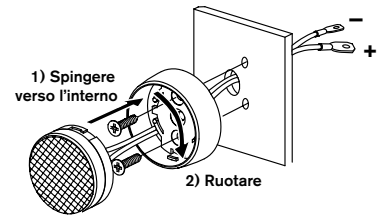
Montaggio a portiera di woofer e tweeter. (TWEETER nella predisposizione nella zona superiore del pannello-portiera WOOFER nella predisposizione del pannello-portiera)
